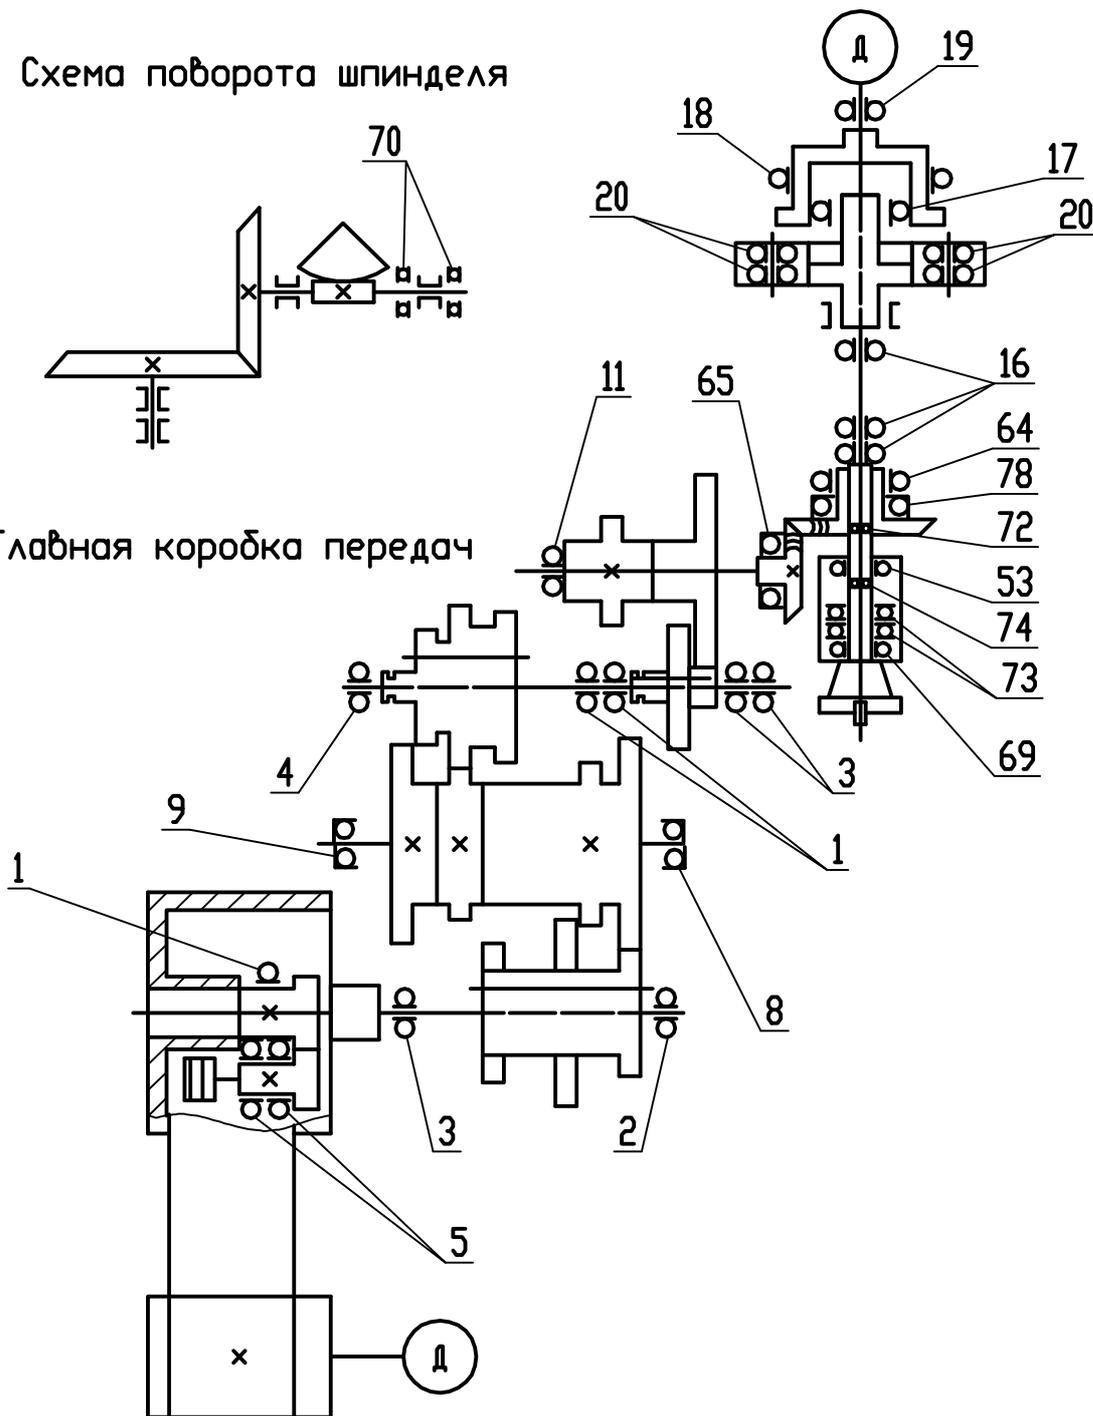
(Лист 1 из 2)- Схема расположения подшипников
